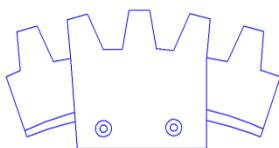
Ремонт зубчатого колеса при помощи башмака
